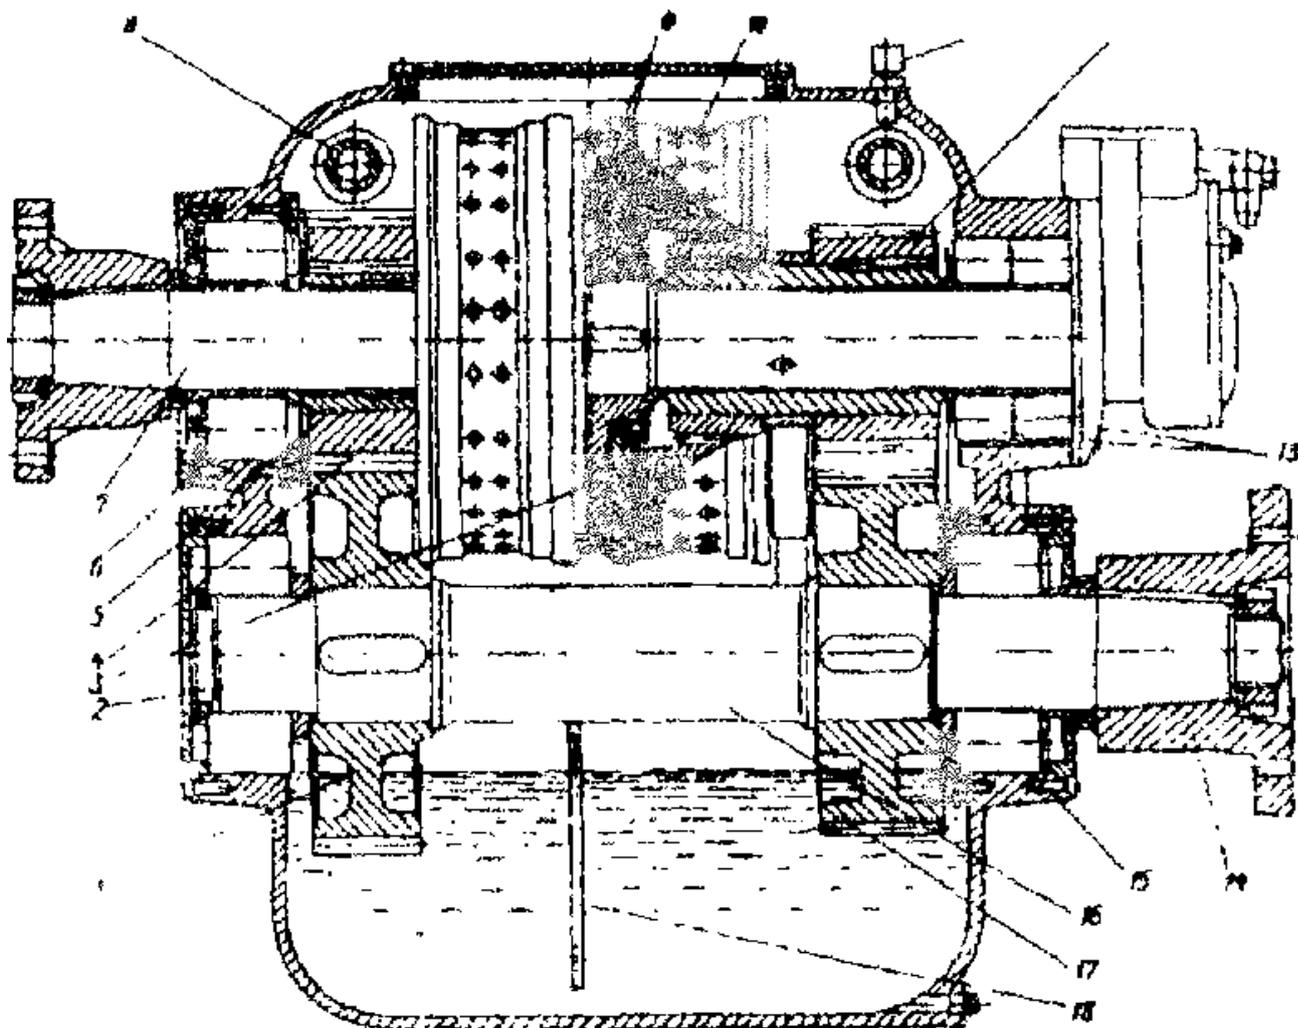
Реверс-редуктор дизеля 6L275PN:
